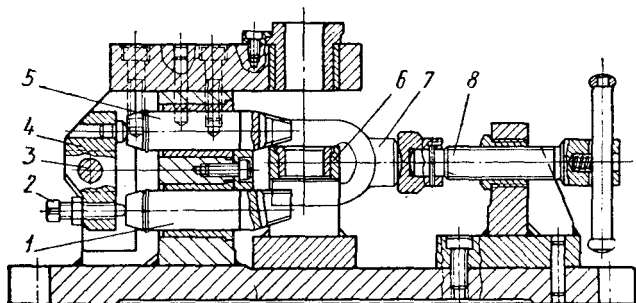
Приспособление с плавающими призмами для обработки отверстий в вилках
